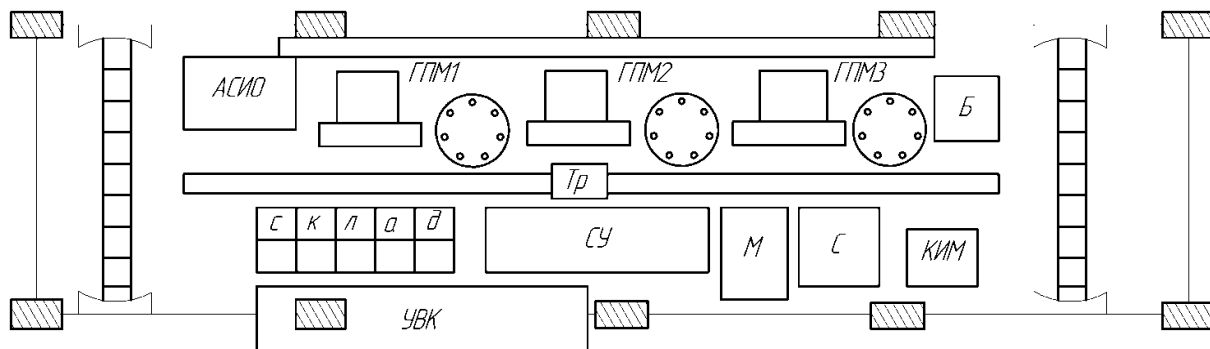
План ГАУ со сверлильно-фрезерно-расточными ОЦ
